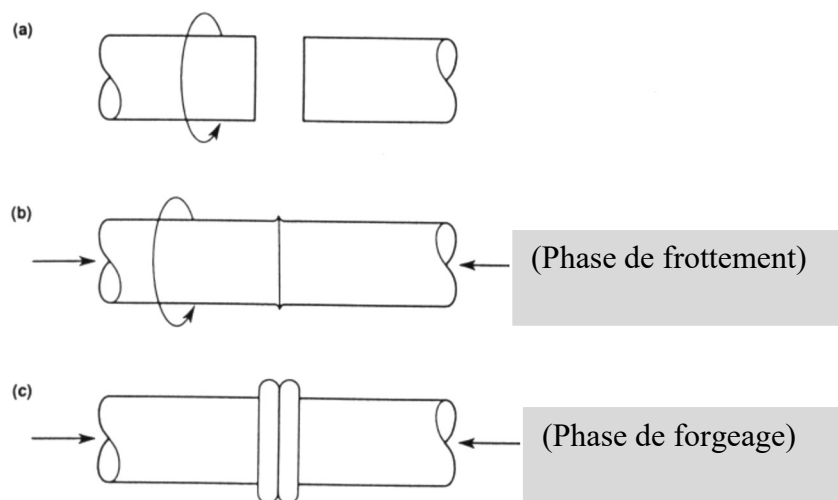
Schéma du procédé de soudage par friction rotative [9].
